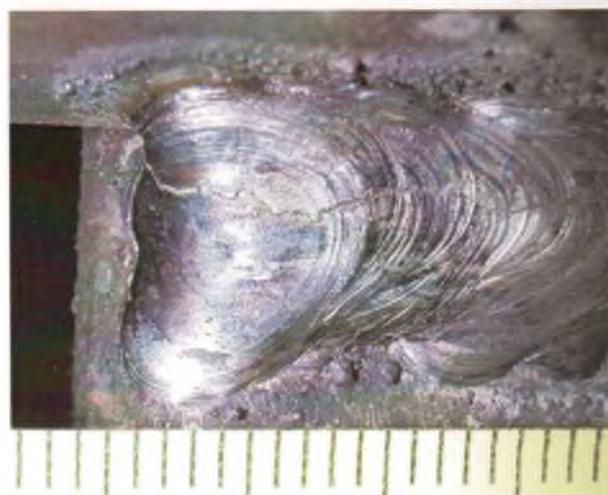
Разветвленная трещина нахлесточного сварного соединения. Детальный вид
